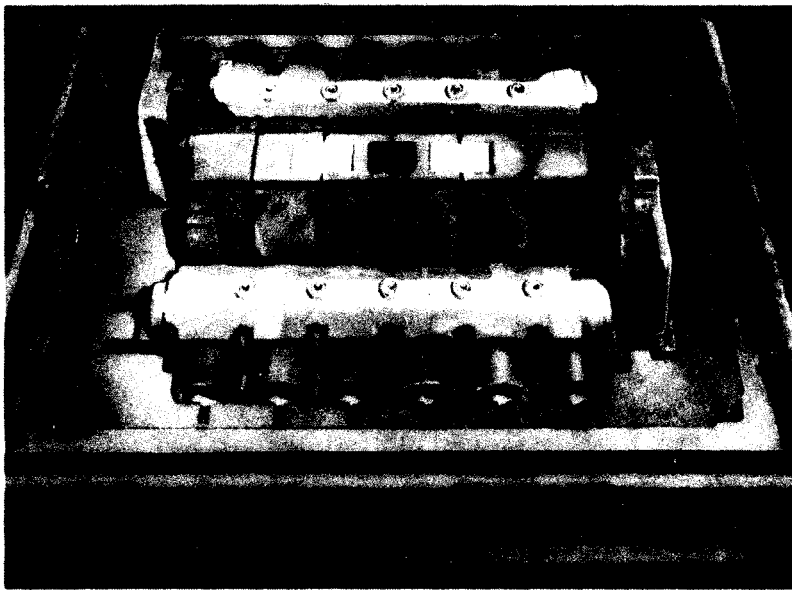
Situación, en la semicaja inferior del molde, de los machos para fundir bloques de seis cilindros (Ford Motor Company).
